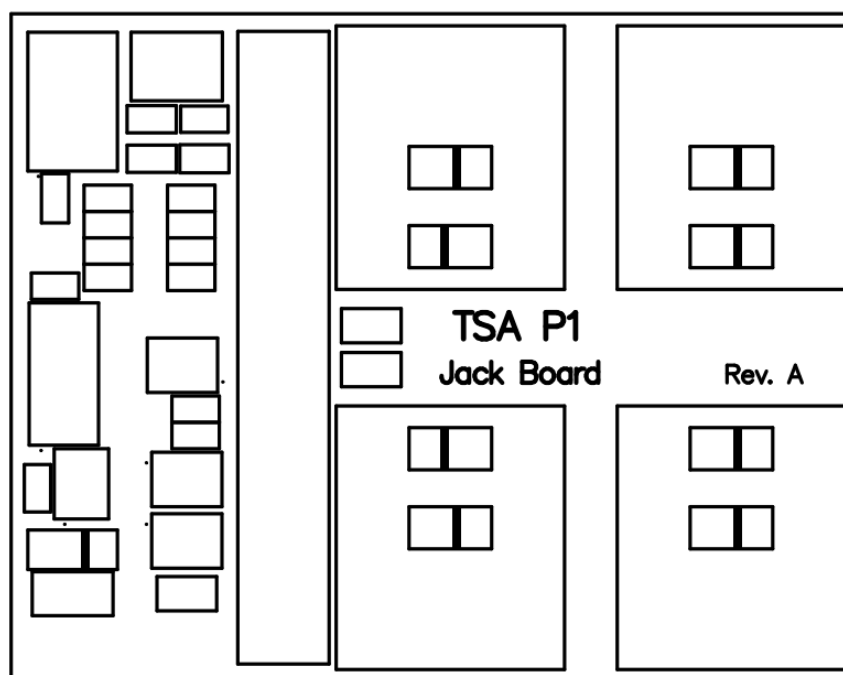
Vodivý motív - prvá vnútorná vrstva (negatívne zobrazenie)
